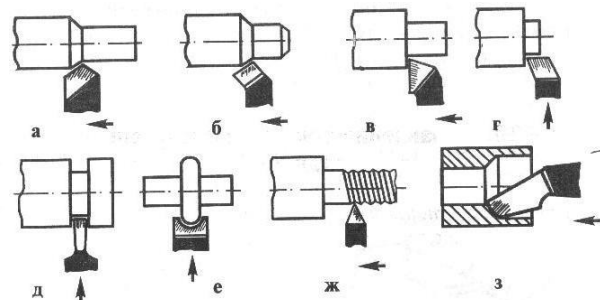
Токарные резцы: а – проходной прямой; б – проходной отогнутый; в – проходной упорный; г – подрезной; д – отрезной; е – фасонный; ж – резьбовой; з – проходной расточной
